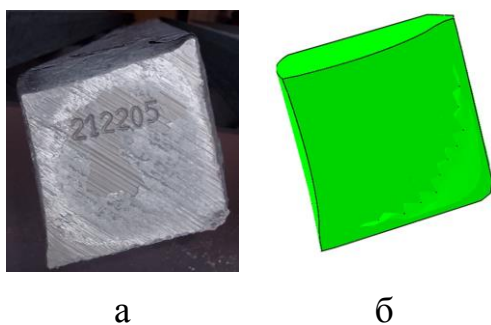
Форма торцевої поверхні безперервнолитої заготовки після поперечного розділення на ножицях (а) і за результатами моделювання (б)
